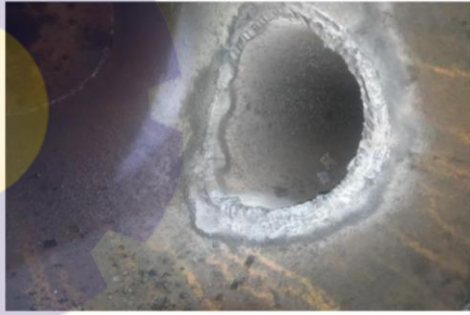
Hasil dari kegiatan *Visual Welding Check
